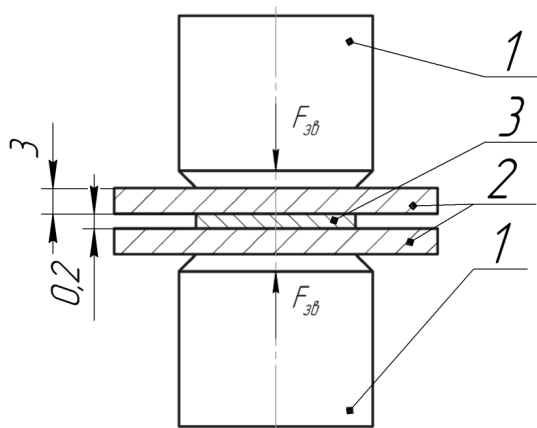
Схема електроконтактного точкового зварювання з використанням багат шарового проміжного прошарку: 1 – електроди (мідь); 2 – деталі (алюміній); 3 – багат шаровий прошарок (алюміній)
